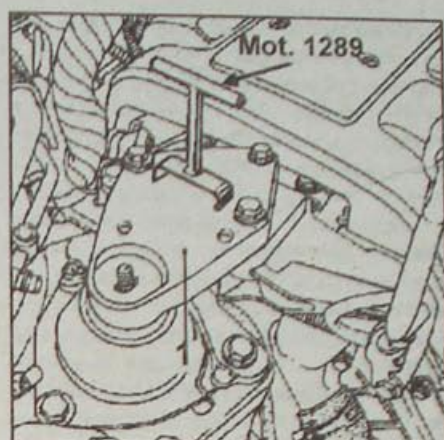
Использование приспособления Mot. 1289-02 для регулировки положения ограничителя хода правой маятниковой подвески двигателя (1)
